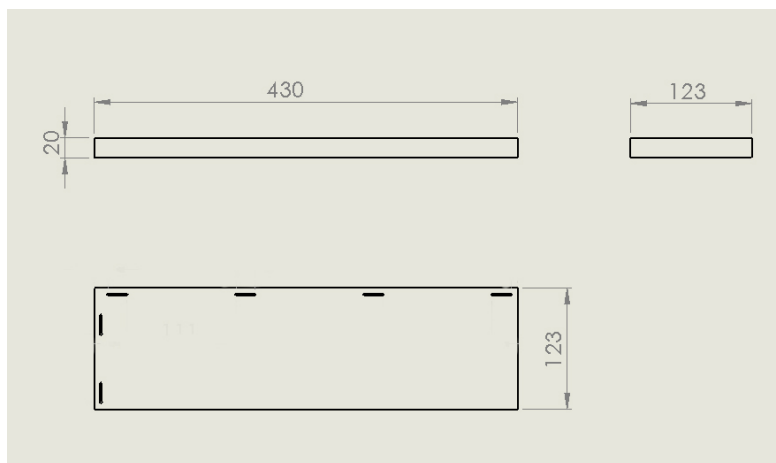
Desenho técnico da placa de 430 x 123 x 20 mm
